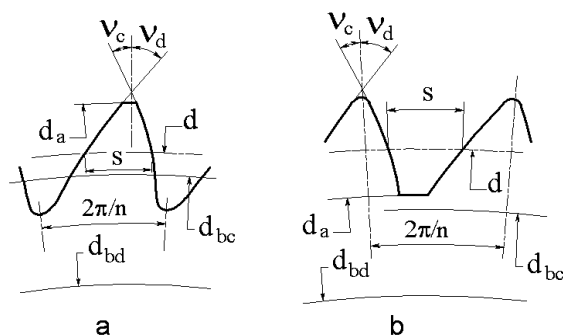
Профиль несимметричного зуба; а – внешний зуб; б – внутренний зуб; d_a , d_b , d – диаметры окружностей вершин зубьев, основной и делительной, соответственно; S – толщина зуба на делительной окружности; v – угол пересечения эвольвентных профилей; "d" и "c" – индексы рабочей и нерабочей сторон несимметричного зуба
